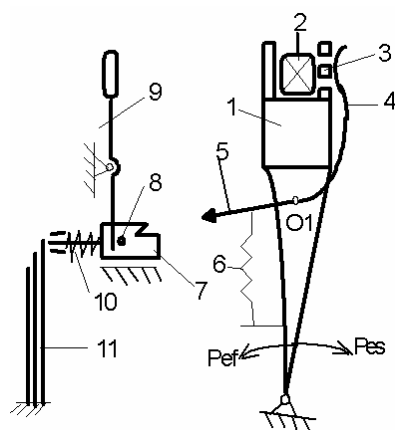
Mecanismul de siguranță cu spată fixă
